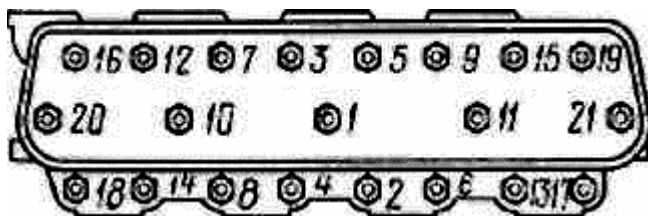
Последовательность затяжки гаек шпилек крепления головок цилиндров двигателей ЯМЗ-238М2.
